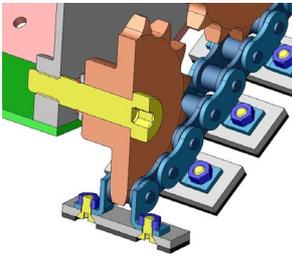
Laufrolle mit Schulterpassschraube
